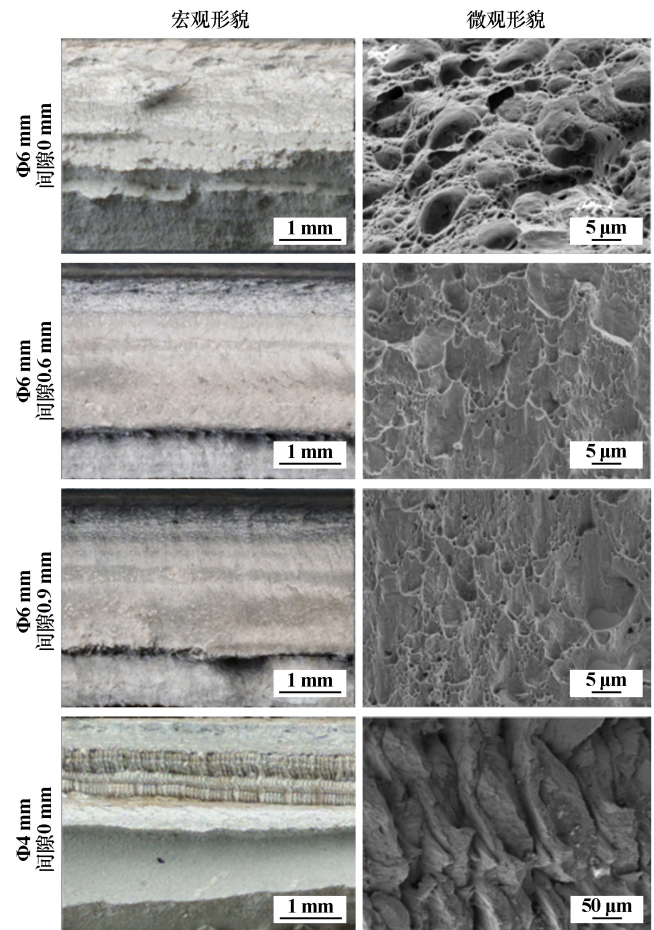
焊接速度 120 mm/min 下焊接头拉伸断口宏观及微观形貌
